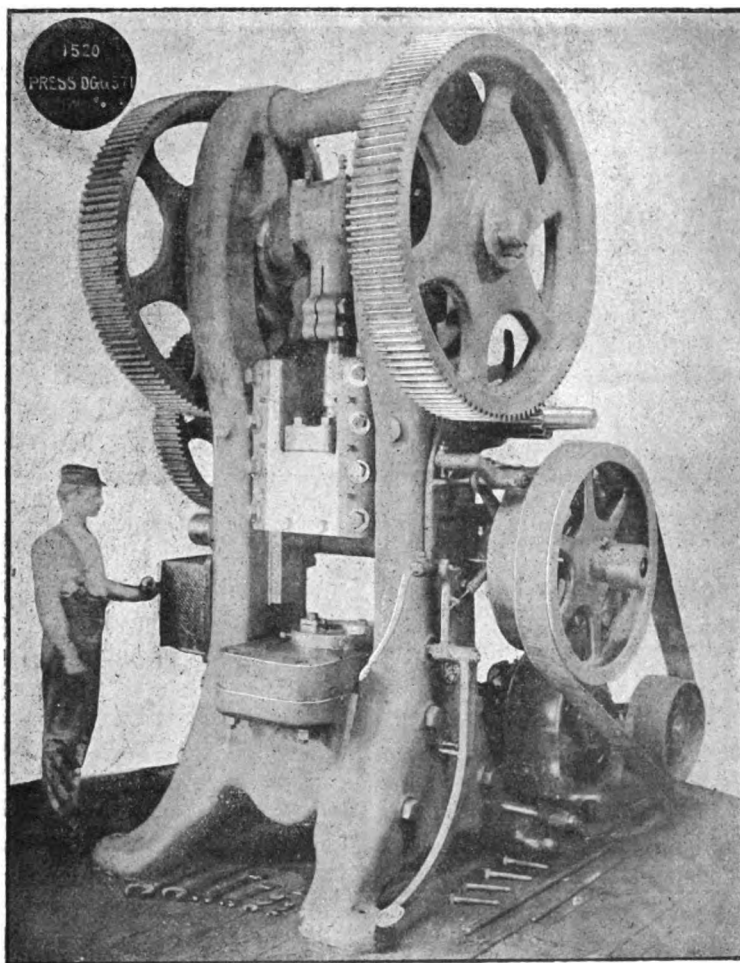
Machine à estamper à triple engrenage et à commande électrique par moteur fixé sur la carcasse de la machine. Poids : 16 000 kg environ.
